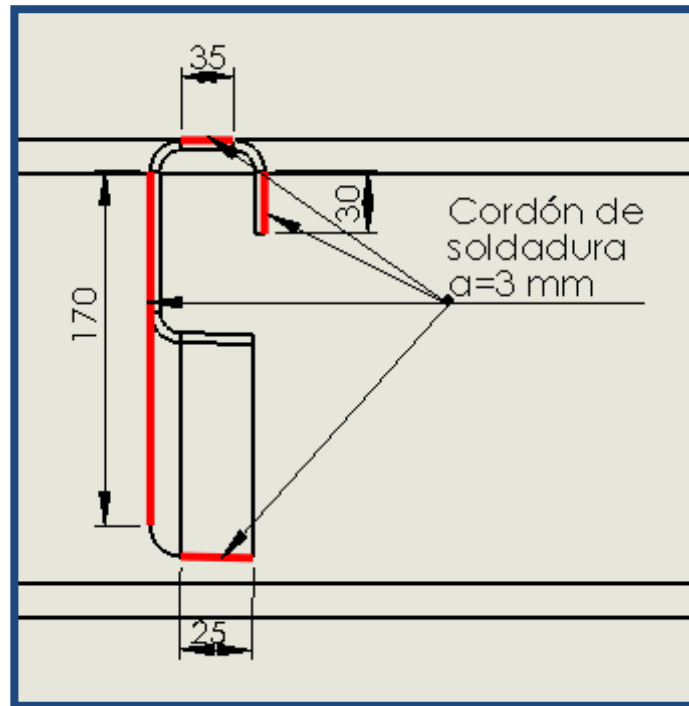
Vista de los cordones de soldadura realizados en la telera.
